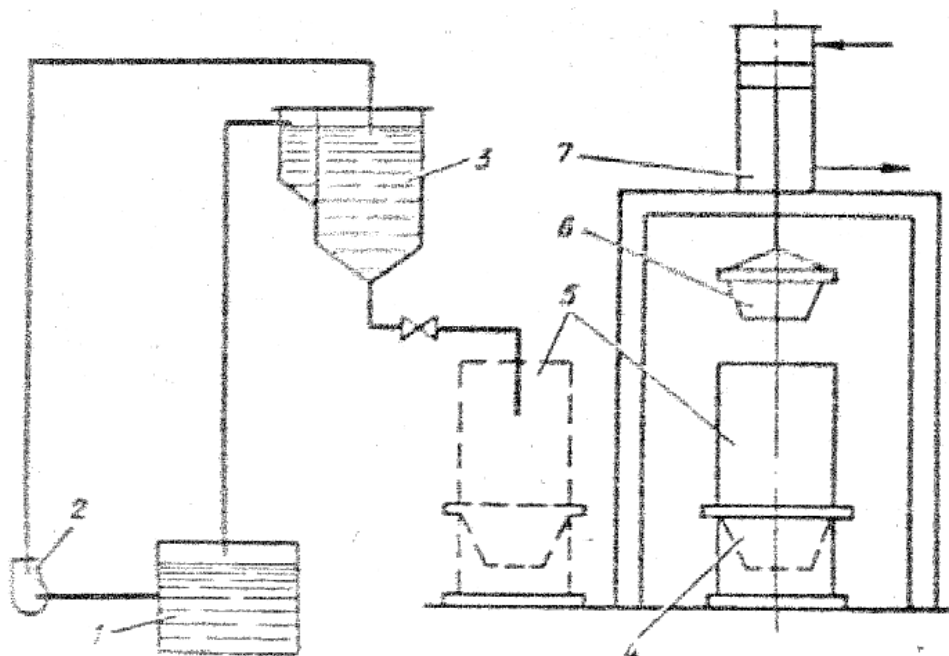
Схема формування литих виробів гідравлічним способом: 1 – ванна з паперовою масою; 2 – насос; 3 – дозатор; 4 – виливна сітчаста форма; 5 – корпус форми; 6 – сітчастий пуансон; 7 – гідравлічний прес
